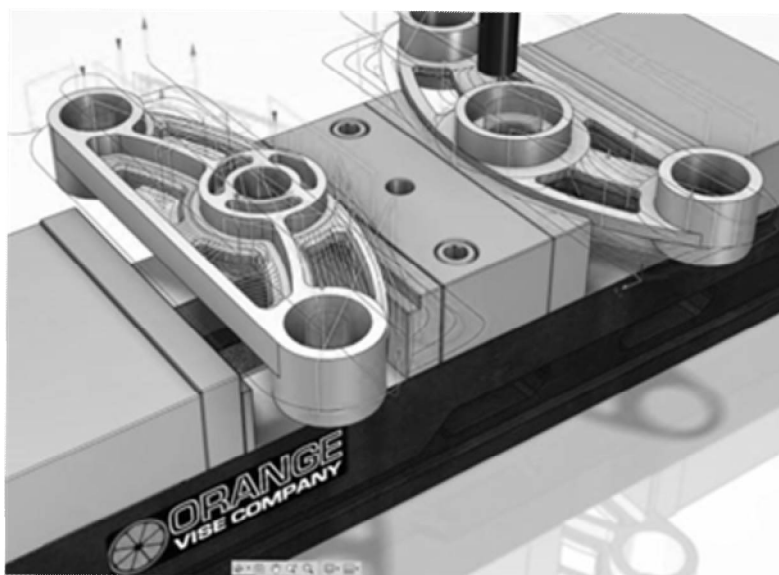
Підготовка траєкторій обробки на верстаті з ЧПК
